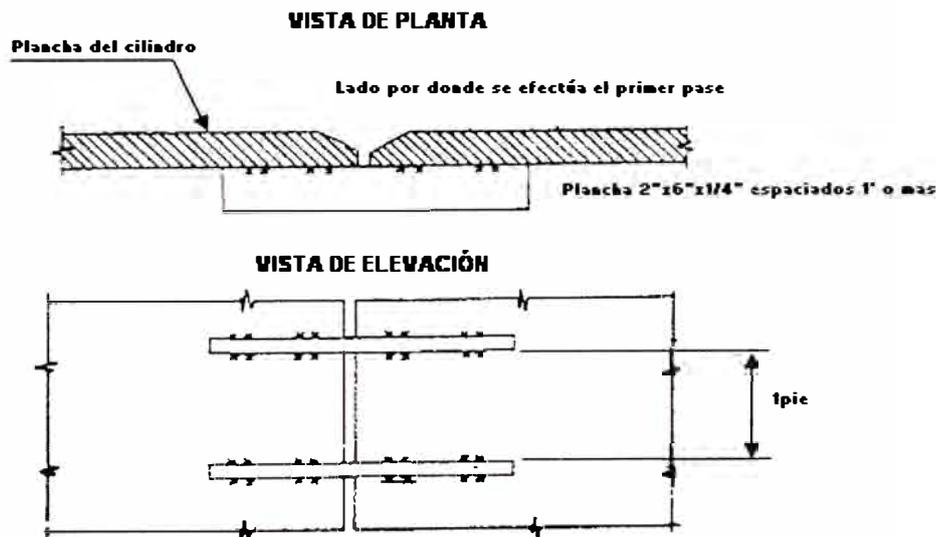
Colocación de platinas "puentes" por la cara interior de las planchas del cilindro
